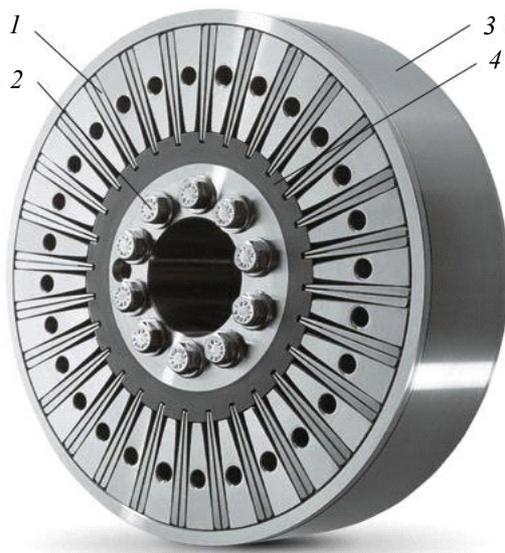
Устройство демфера Geislinger модели D60/14/2: 1 – пакет пружинных пластин; 2 – болты крепления корпуса демфера к валу двигателя; 3 – внешний обод демфера; 4 – корпус демфера
